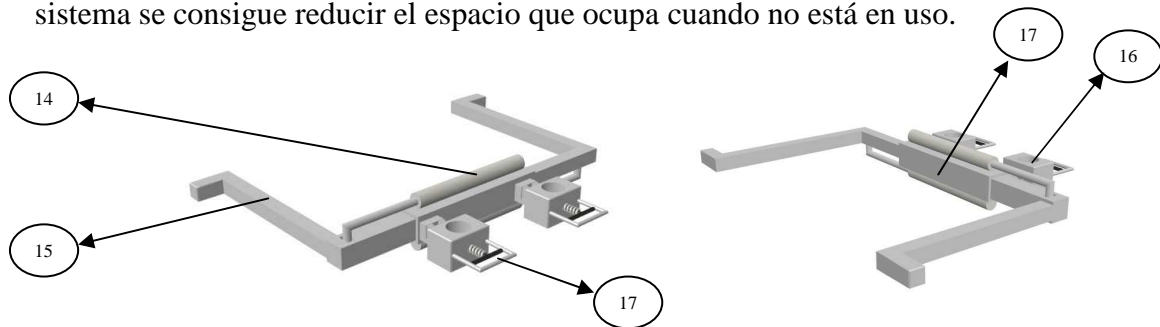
Parte central: estructura de los ganchos vista desde atrás y delante
